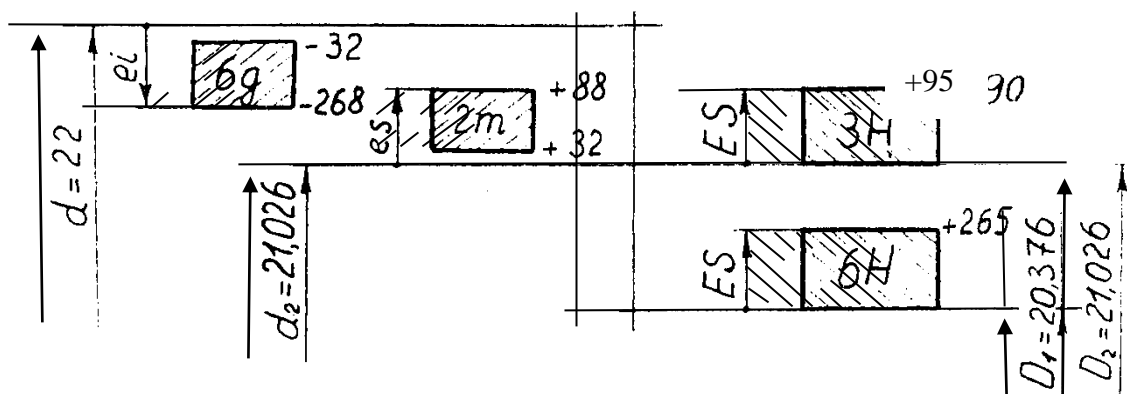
Схема расположения полей допусков метрической резьбы с переходной посадкой
